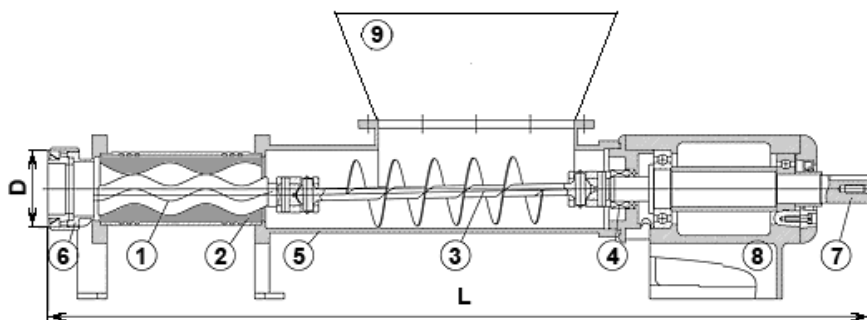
Схема устройства ВН CFS: 1 – винт; 2 – обойма; 3 – шнек; 4 – торцовое уплотнение; 5 – корпус насоса; 6 – выходной фланец; 7 – приводной вал; 8 – корпус подшипников, 9 – бункер
